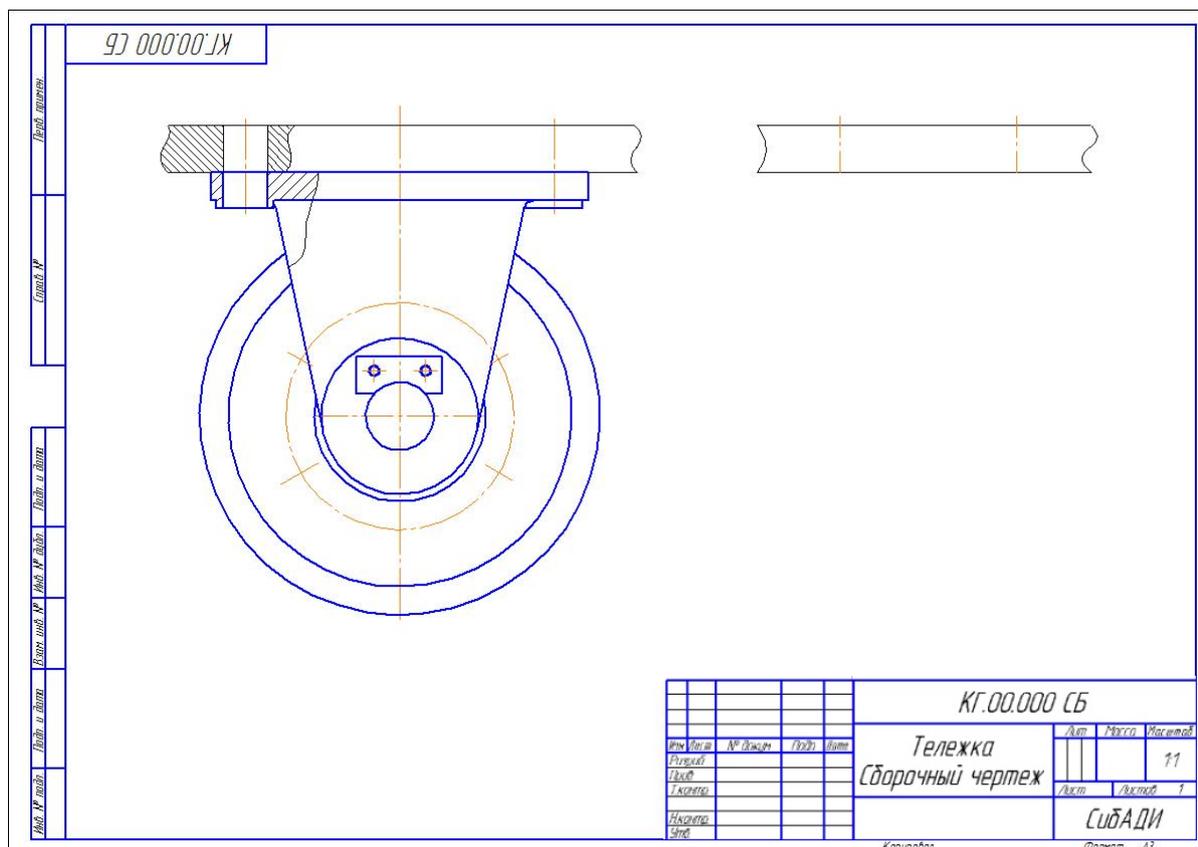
Заготовка сборочного чертежа изделия «Тележка»
